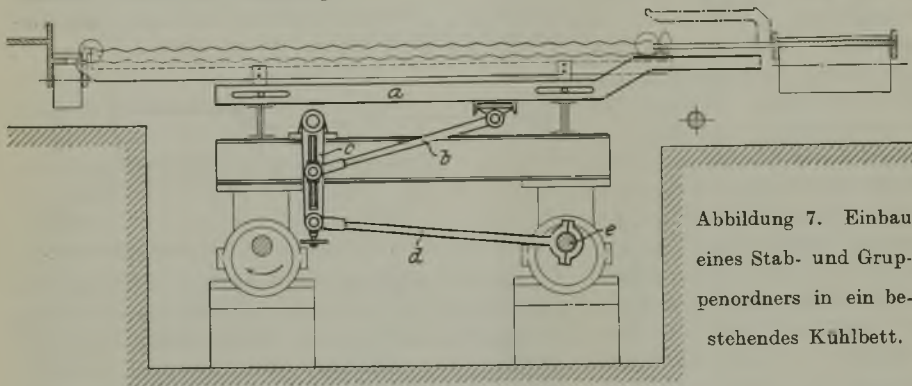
Einbau eines Stab- und Gruppenordners in ein bestehendes Kühlbett.
